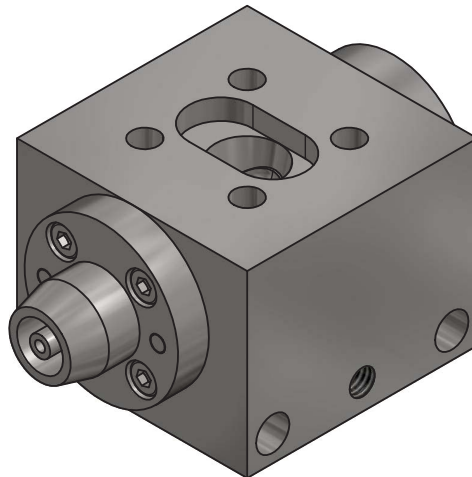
Technische Zeichnung der Schlauchdüse
